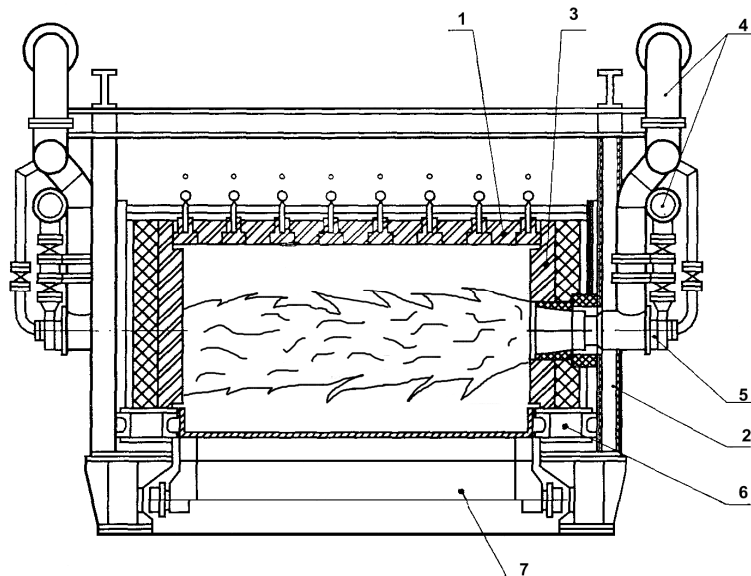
Камерный зажигательный горн с боковыми горелками
